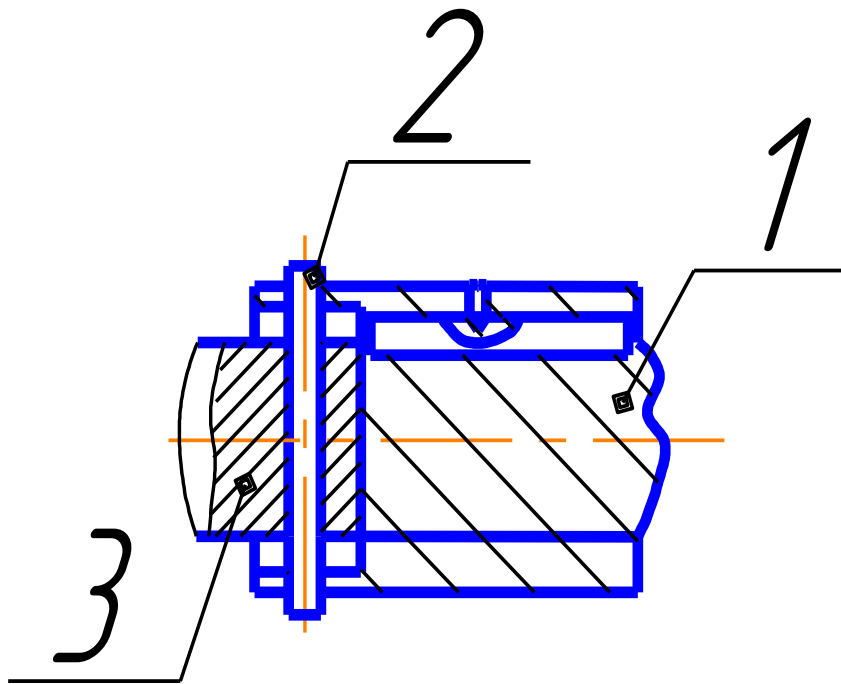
Схема з'єднання ножевого валу та приводного валу
